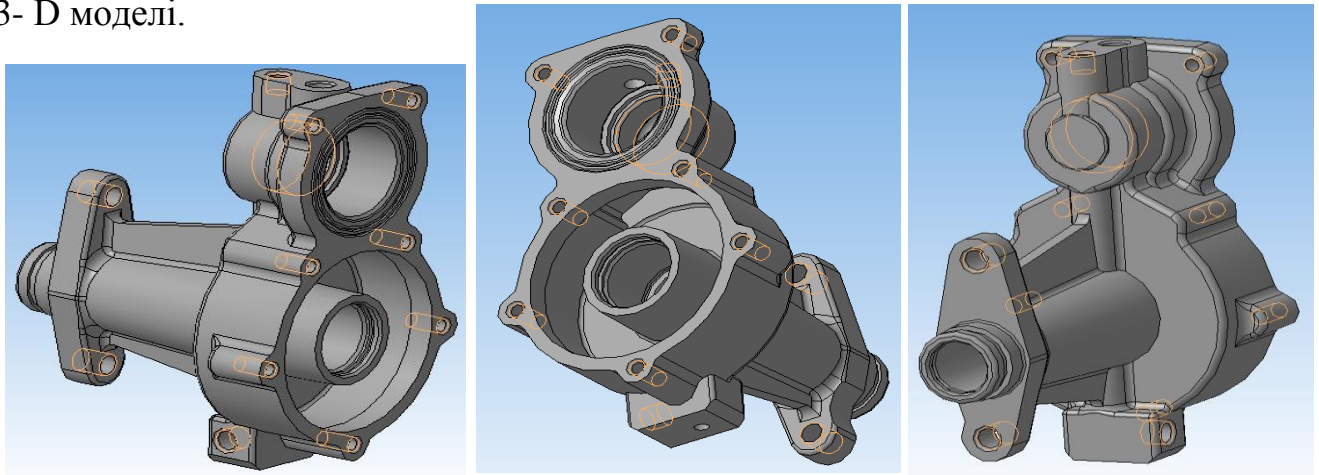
3-D модель деталі «Корпус задній пневматично-гідравлічного підсилювача зчеплення»
